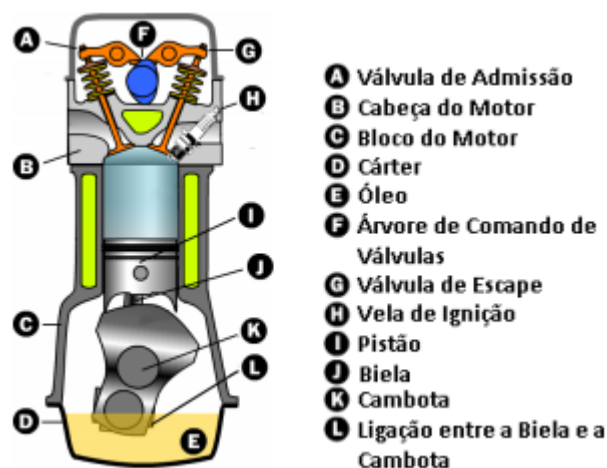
Esquema representativo de um motor de combustão interna [8].
